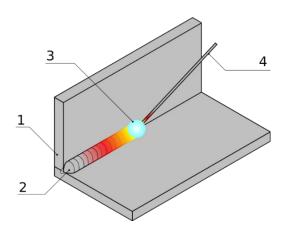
Esquema soldadura. Fuente: Wikipedia.org
